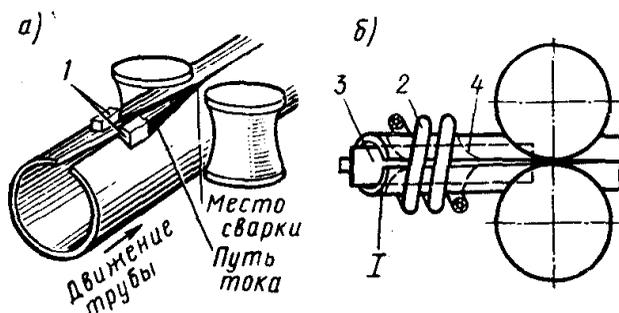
Схема контактной сварки труб токами высокой частоты:
